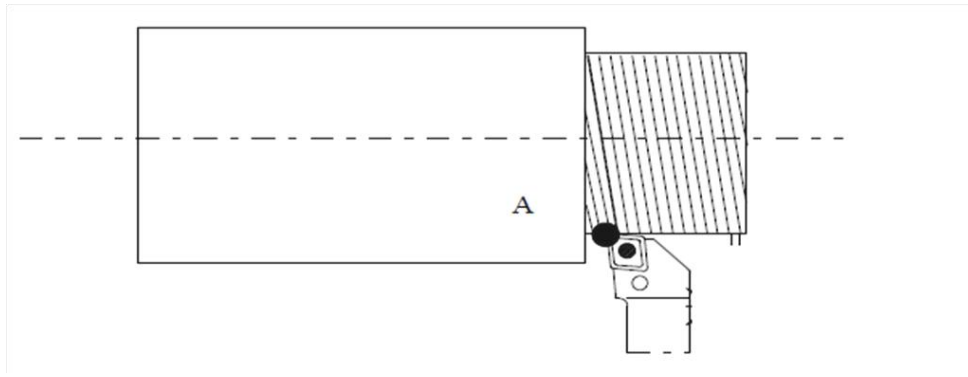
Vitesse de coupe d'un outil de tournage [4].
